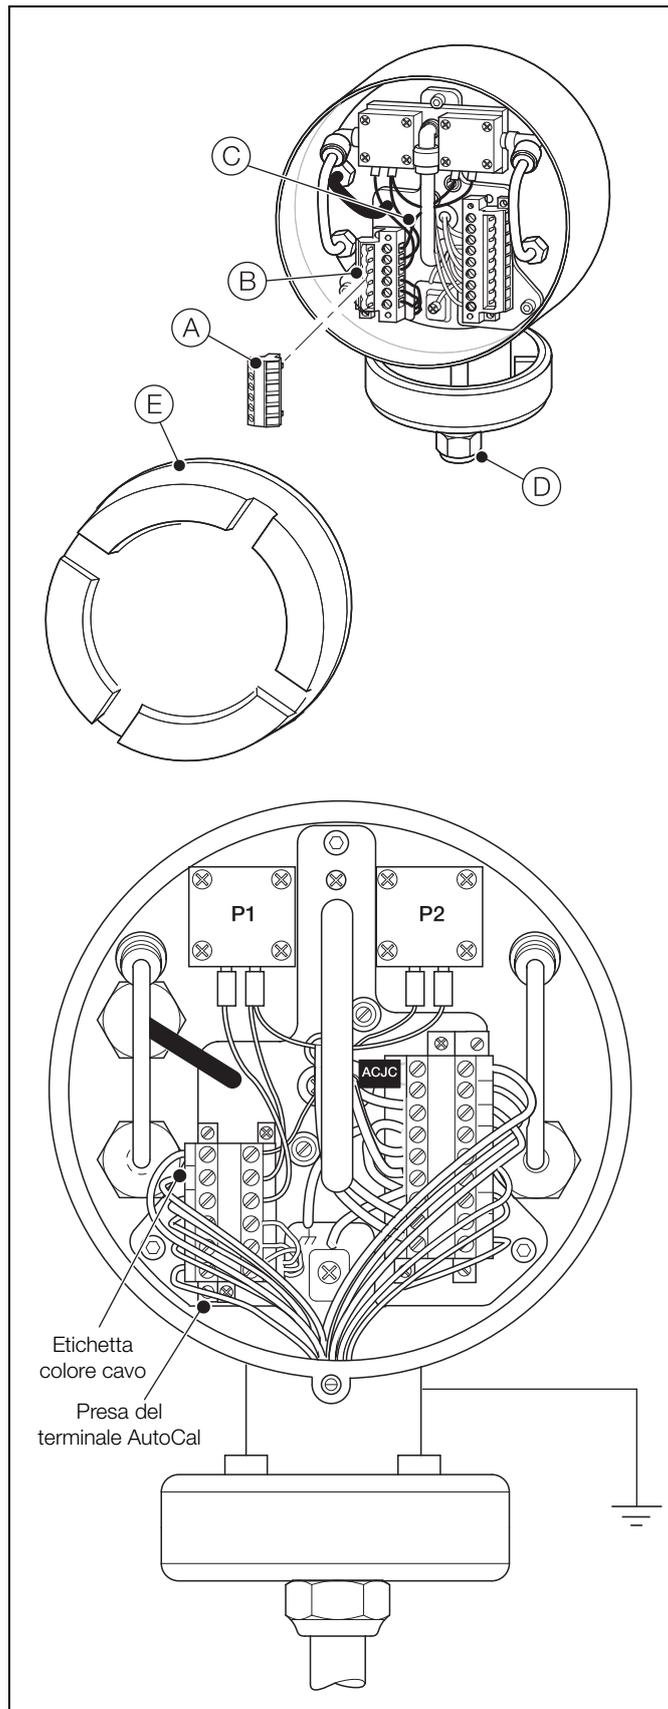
Collegamenti AutoCal sulla sonda Endura AZ30
